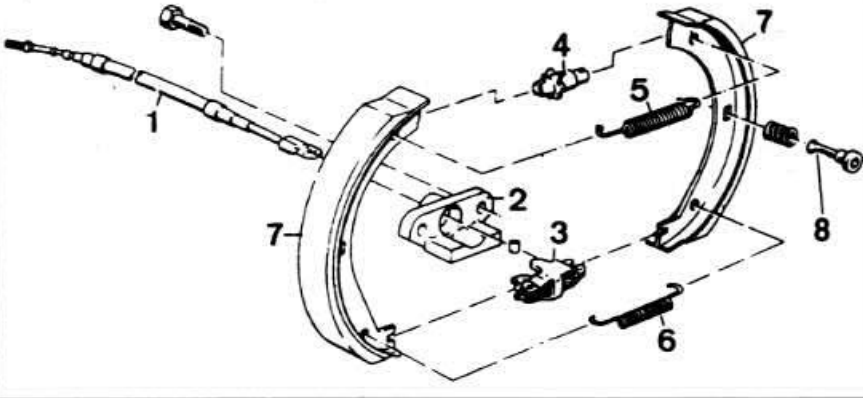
Привод стояночного тормоза автомобилей с барабанным тормозным механизмом задних колес:
